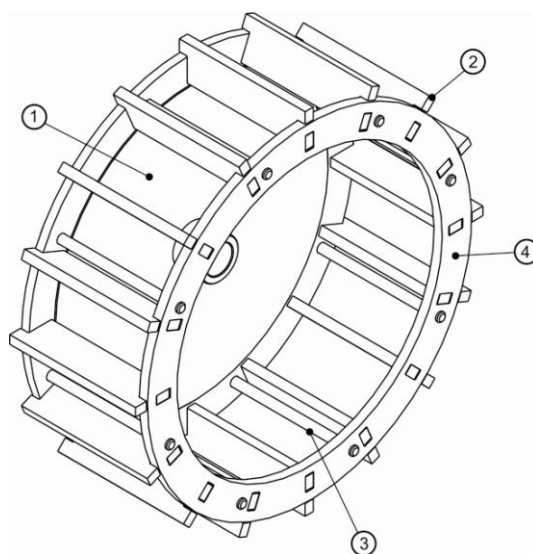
Делительный ротор динамического воздушно-центробежного классификатора
